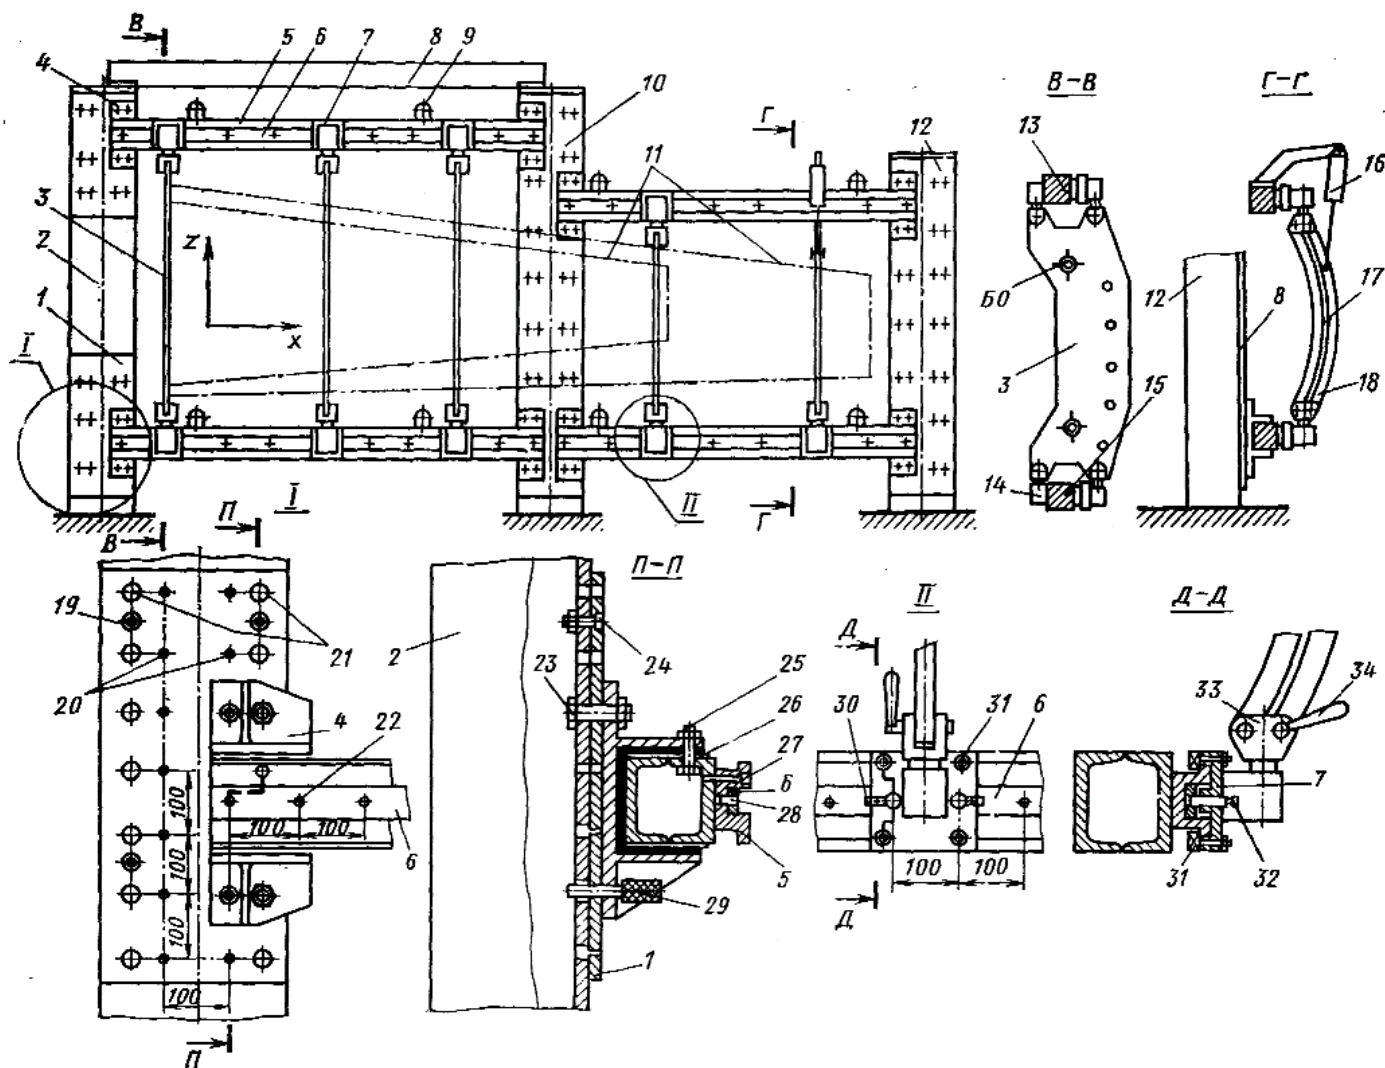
Специализированное сборочное приспособление для сборки группы панелей:
